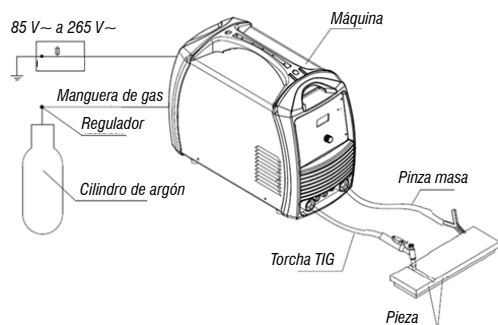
Montaje del conjunto para soldadura TIG
